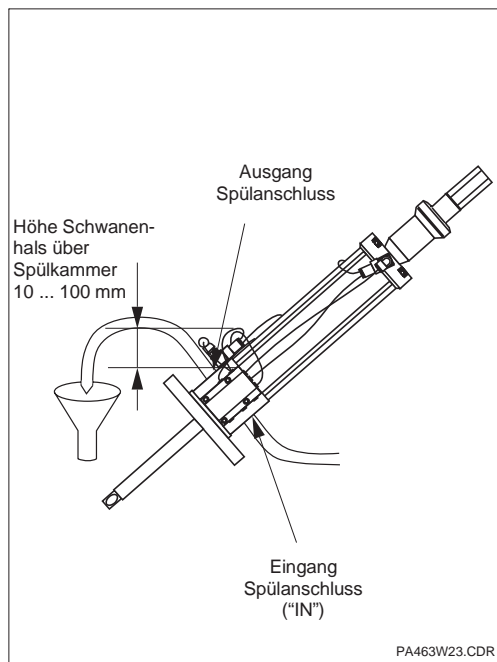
Armatureneinbau bei Benutzung des Spülanschlusses
